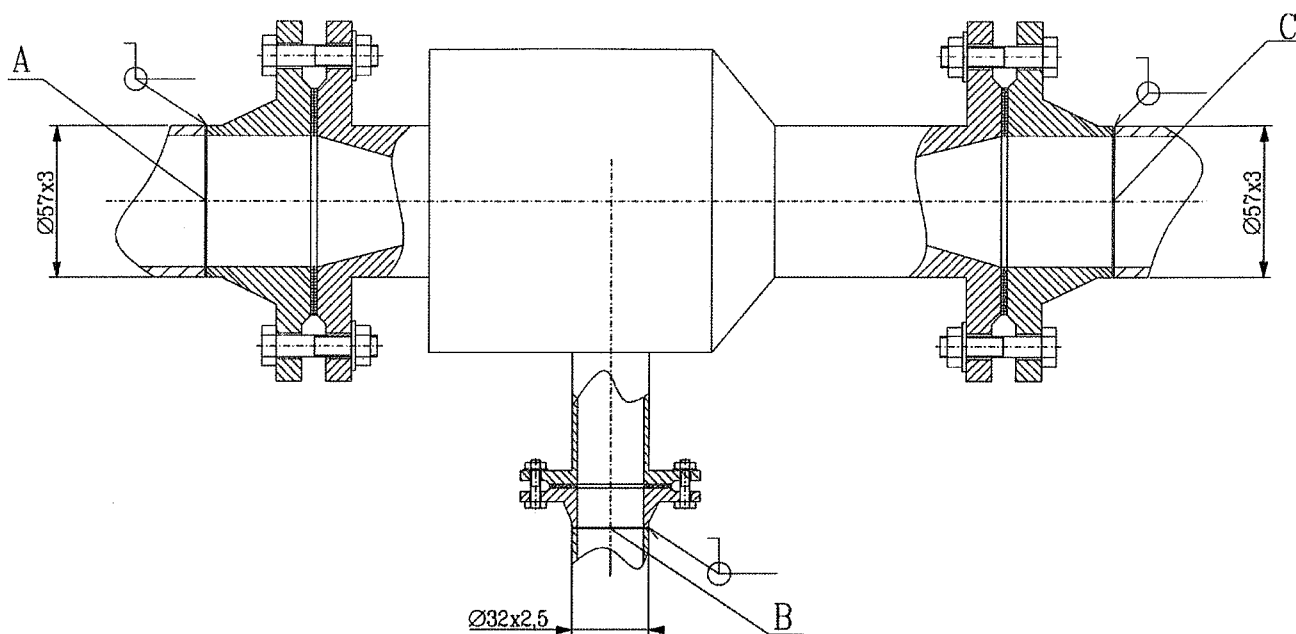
Габаритный чертеж эжектора приема этаноламина QCR10BN001
